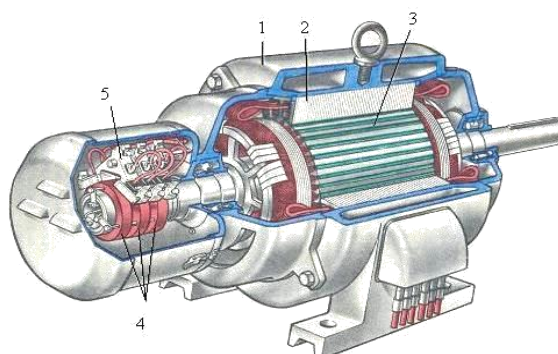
Устройство асинхронного двигателя с фазным ротором 1 – станина, 2 – обмотка статора, 3 – ротор, 4 – контактные кольца, 5 – щетки.
